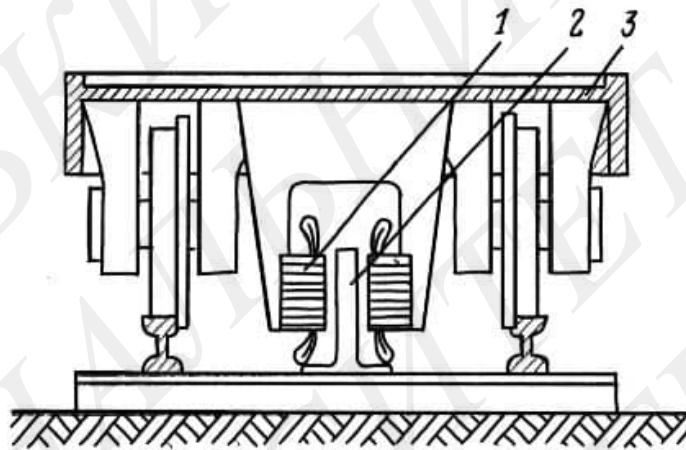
Конструктивна схема з'єднання лінійного двигуна
